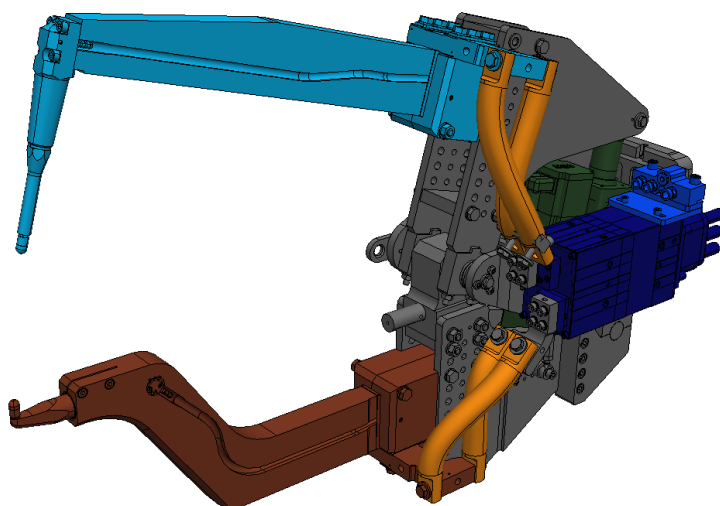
Сварочный пистолет X типа для 5080R02 Z
